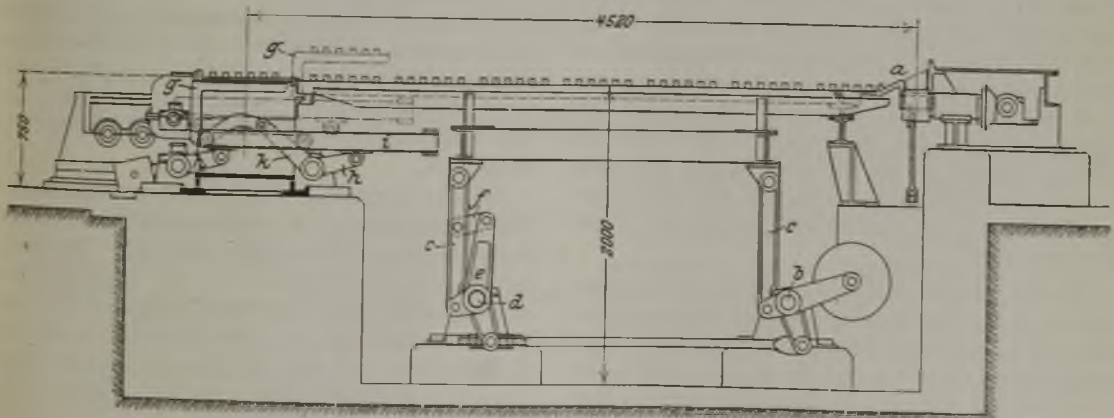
Mechanisches Kühlbett, Bauart Noll, Ausführung Kalker Maschinenfabrik.
